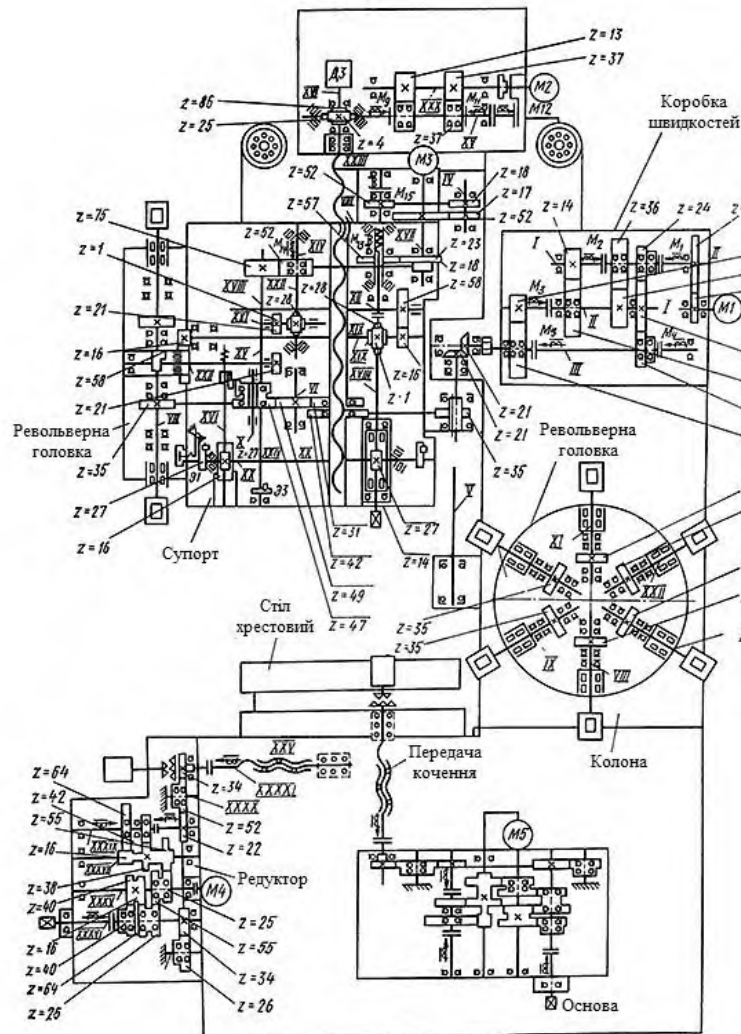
Кінематична схема свердильного верстата 2Р135Ф2
